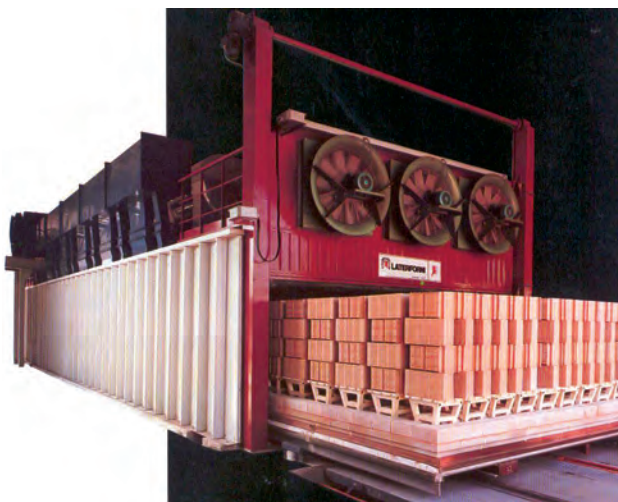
Tunnelofentüre mit eingebauten Schiebeluftventilatoren
